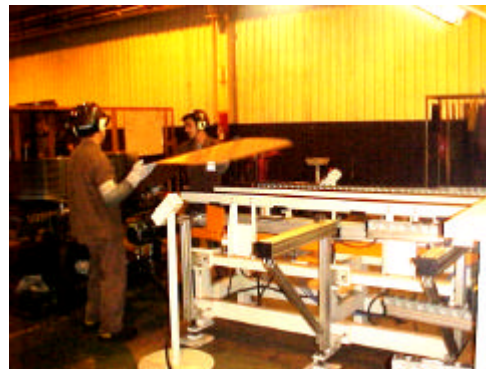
Retirada do Tailored Blank no processo de soldagem
